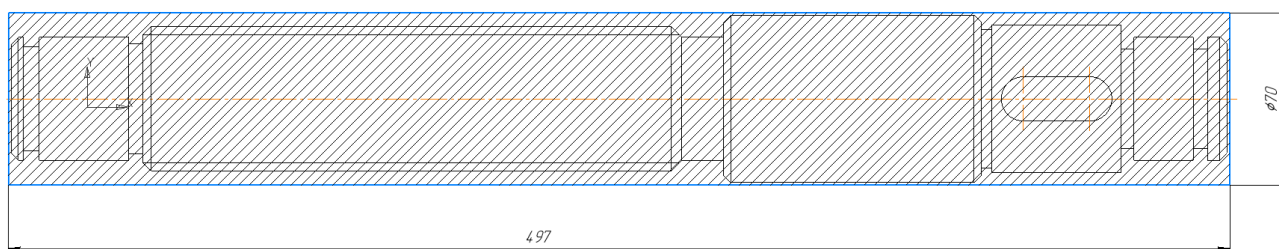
Ескіз заготовки виготовленої з прокату
